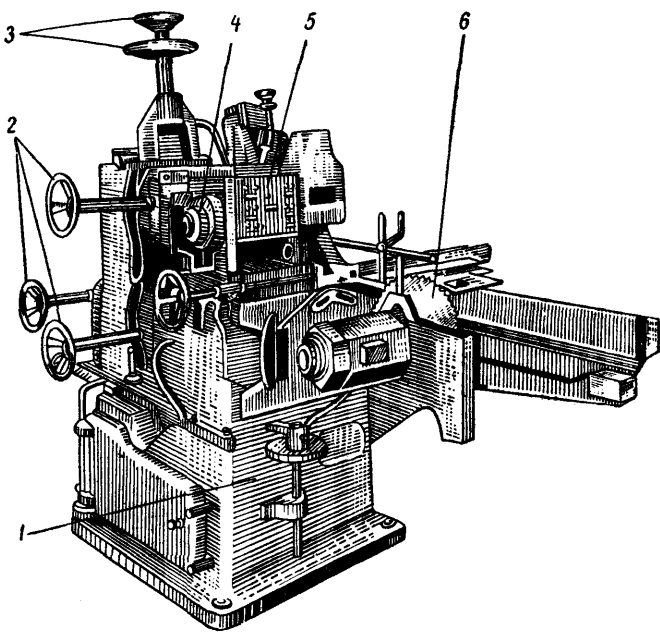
Шипорезный станок ШО-6 с ручной подачей:
